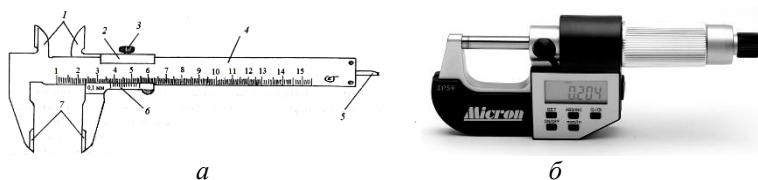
Штангенциркули: а – нониусный (ЩЦ1);
